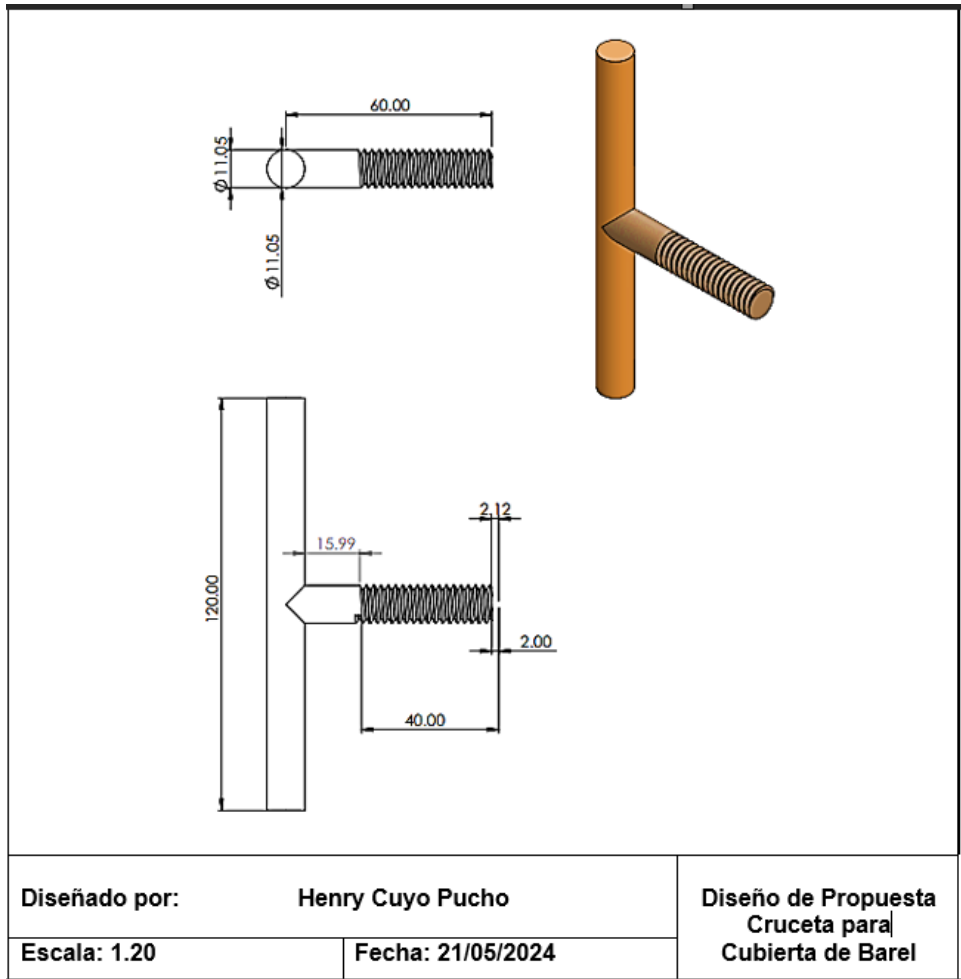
Plano de cruceta para armado de Covered Base for Barel – CBB.
